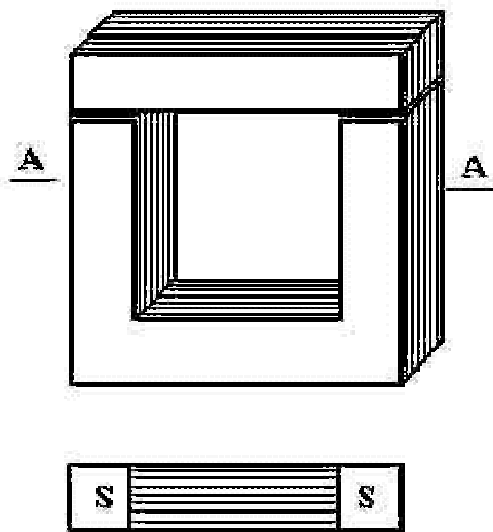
Vista y corte de un núcleo tipo apilado
